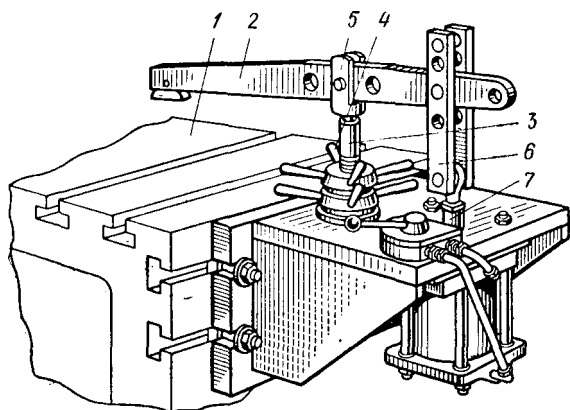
Универсальный пневматический силовой привод к радиально-сверлильным станкам
